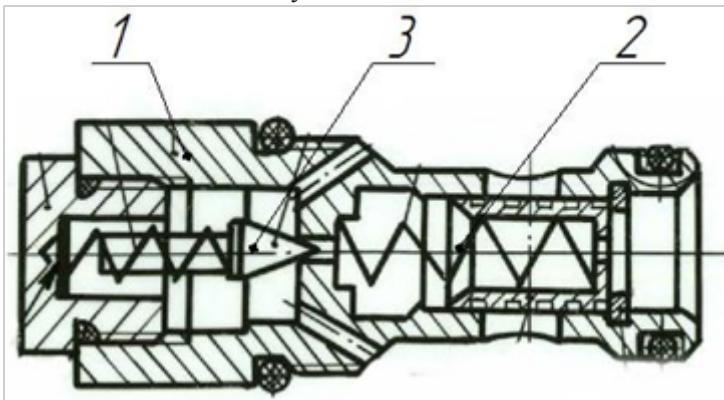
Клапан непрямої дії 1 – корпус; 2 – головний клапан;
